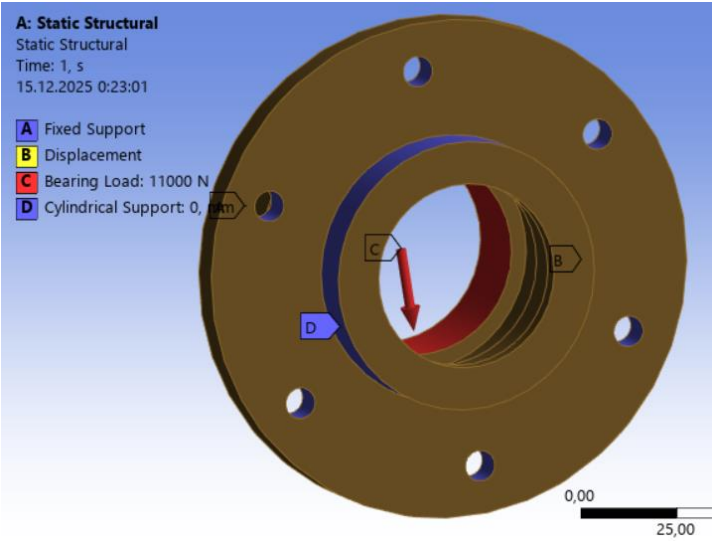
Розрахункова модель корпусної деталі з граничними умовами
